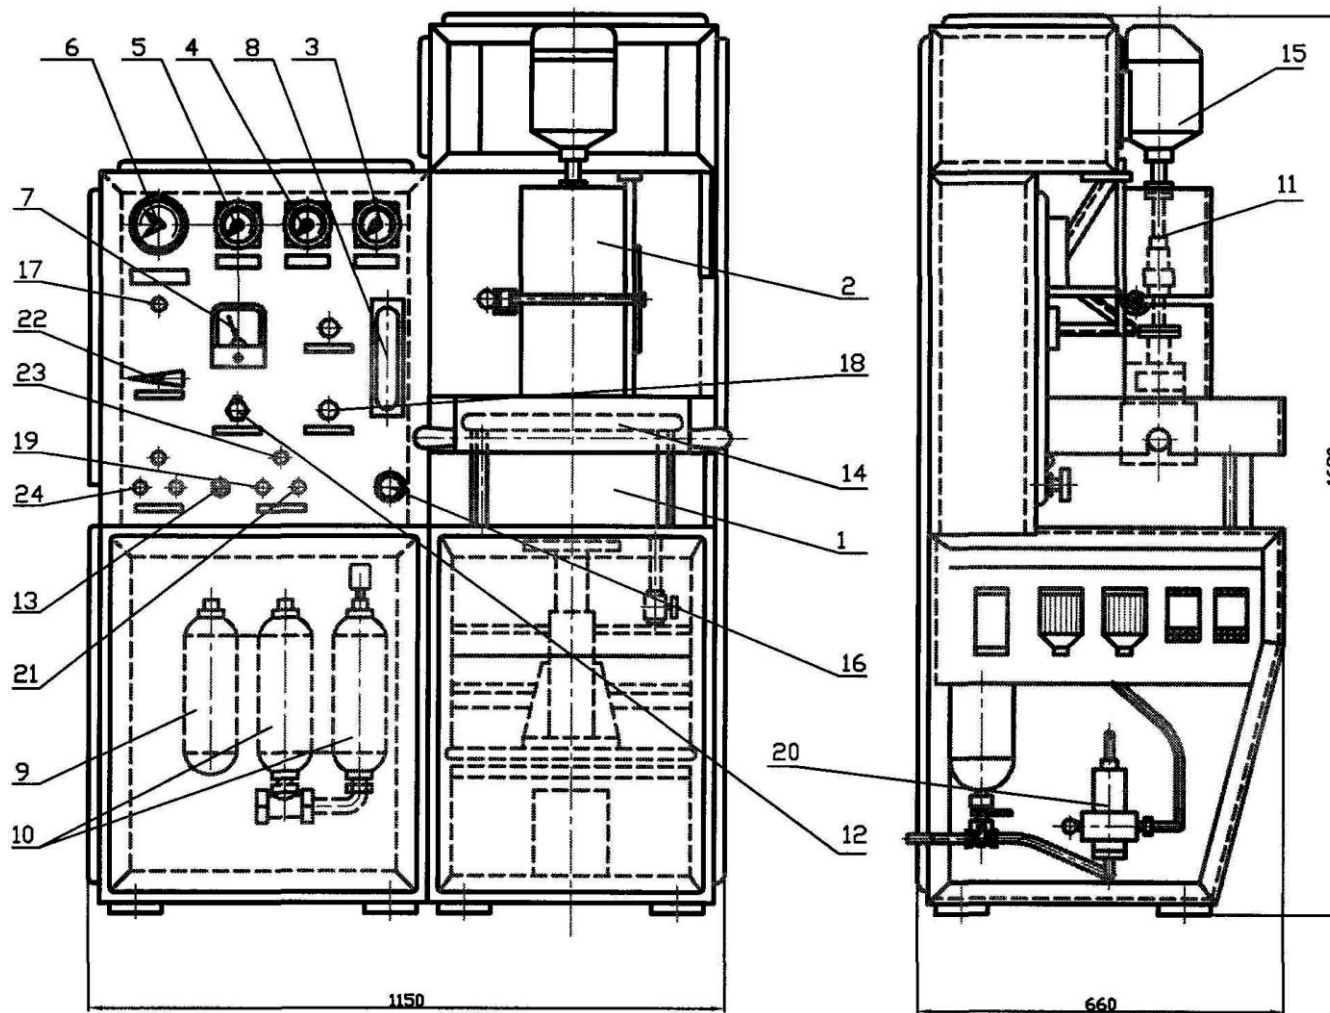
Стенд для перевірки компресора на продуктивність: 1 – обкаточна ванна; 2 – захисний щиток; 3, 4 – манометр; 5 – мановакуумметр; 6 – ТПГСКП0...100; 7 – ватметр; 8 – ротаметр; 9 – ресивер; 10 – масловідділювач; 11 – телескопічний вал; 12 – тумблер; 13 – вентиль; 15 – електродвигун обкатки; 16 – вентиль регулювальний; 17, 18, 23 – лампа сигнальна; 19 – кнопка «Пуск»; 20 – регулятор тиску обкатки; 21 – кнопка «Стоп»; 22 – вимикач мережі; 24 – кнопка «Пуск»
